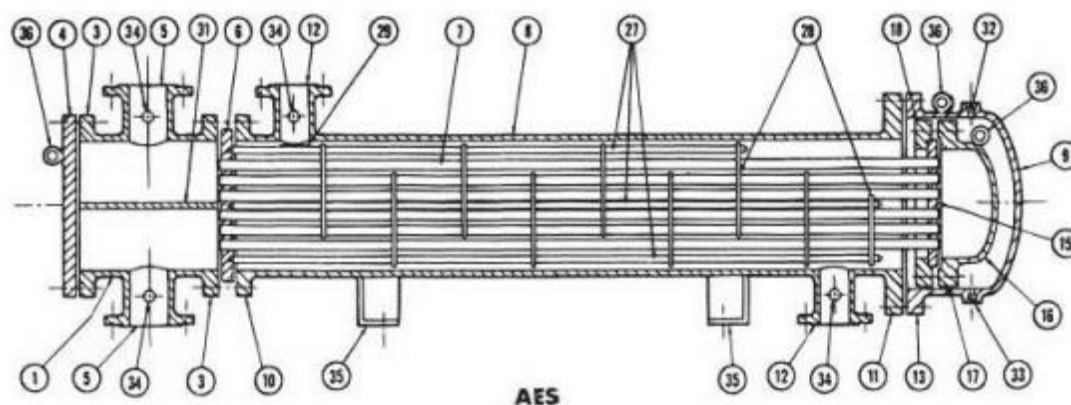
Кожухотрубчатый теплообменник с плавающей головкой.
